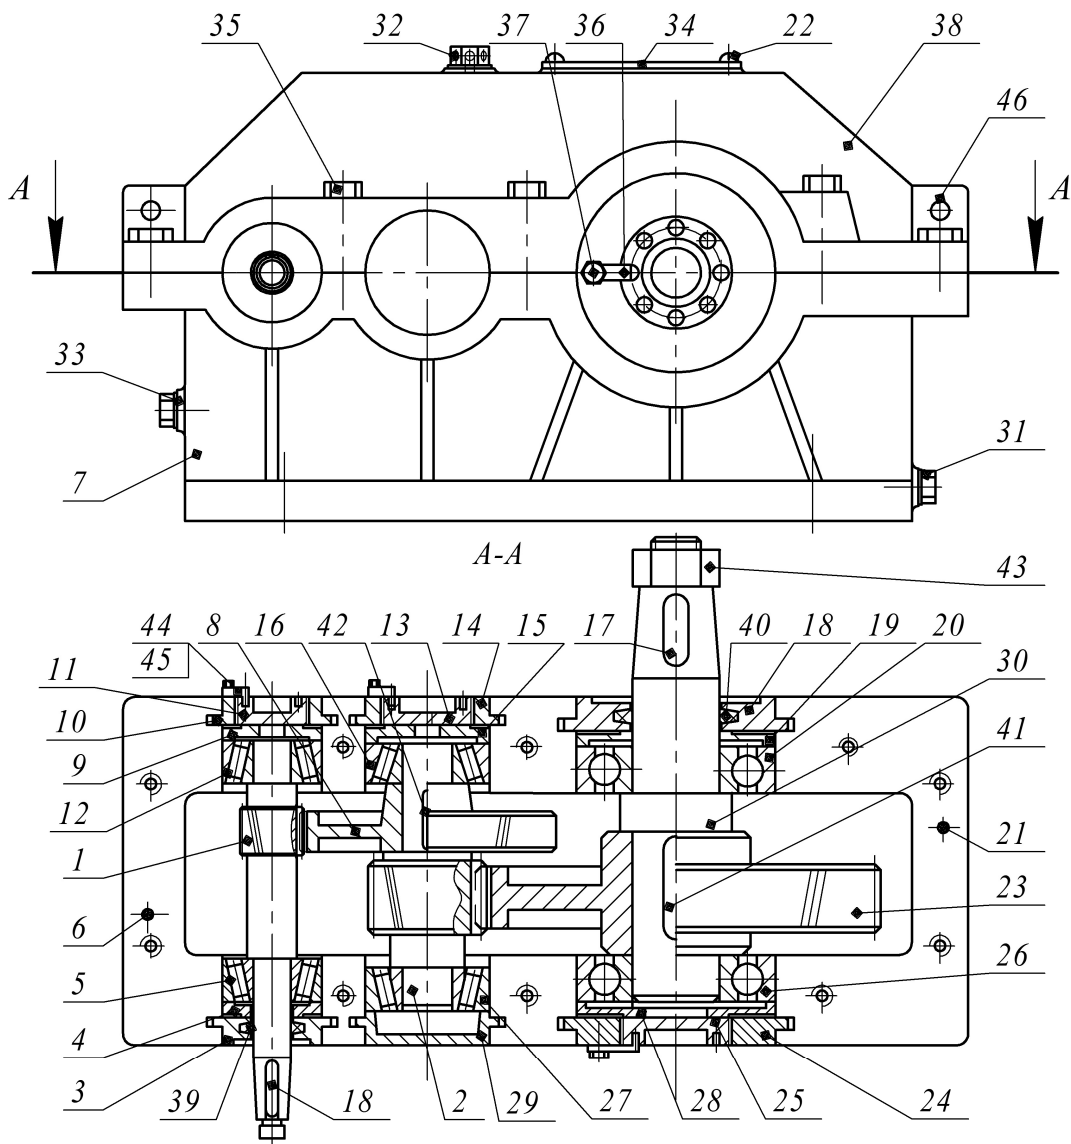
Конструкция цилиндрического двух ступенчатого редуктора:
